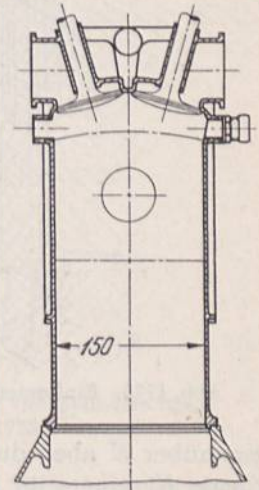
Leichtmotorzylinder mit schräg angeordneten Ventilen im Kopf.
